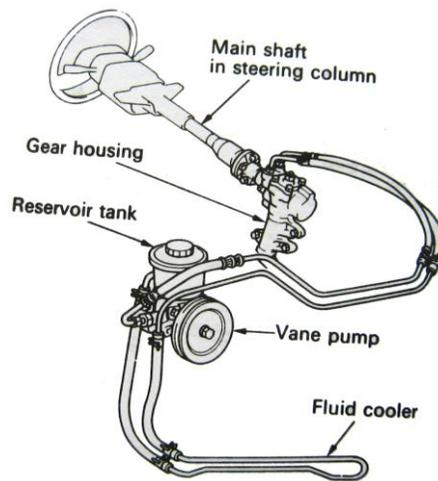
Recirculating Ball Steering Gear untuk Suspensi Rigid
